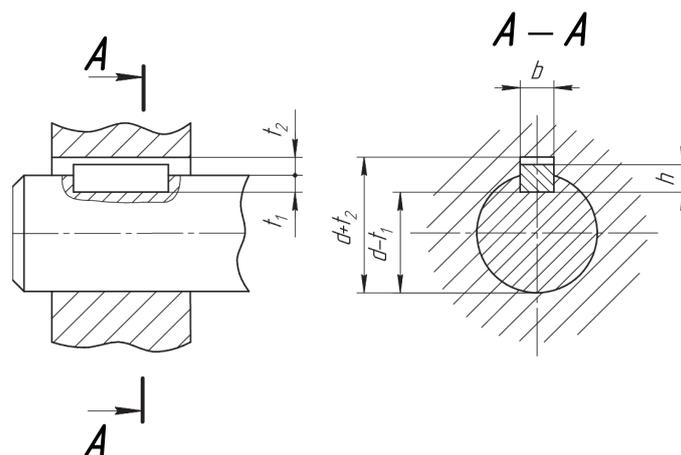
Обозначение основных геометрических параметров шпоночного соединения с призматической шпонкой
